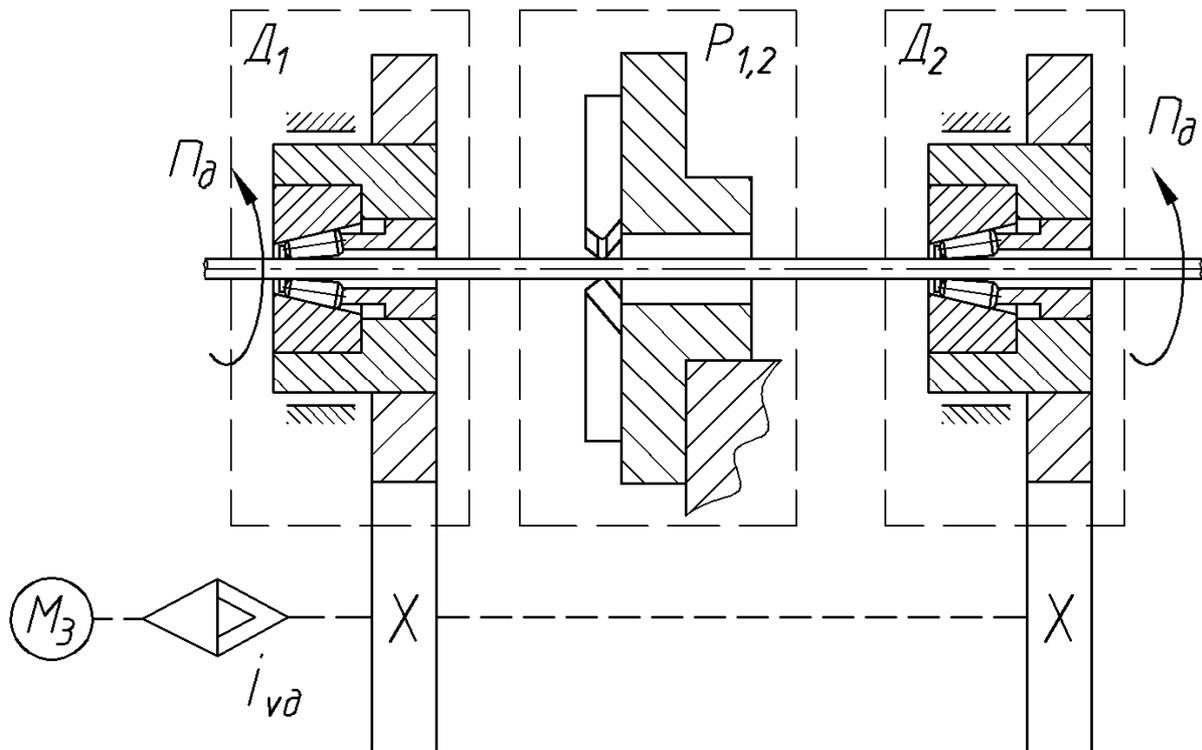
Конструктивная схема совмещенной обработки резанием и ППД роликами с самоподачей заготовки двумя обкатниками при неподвижной резцовой головке
